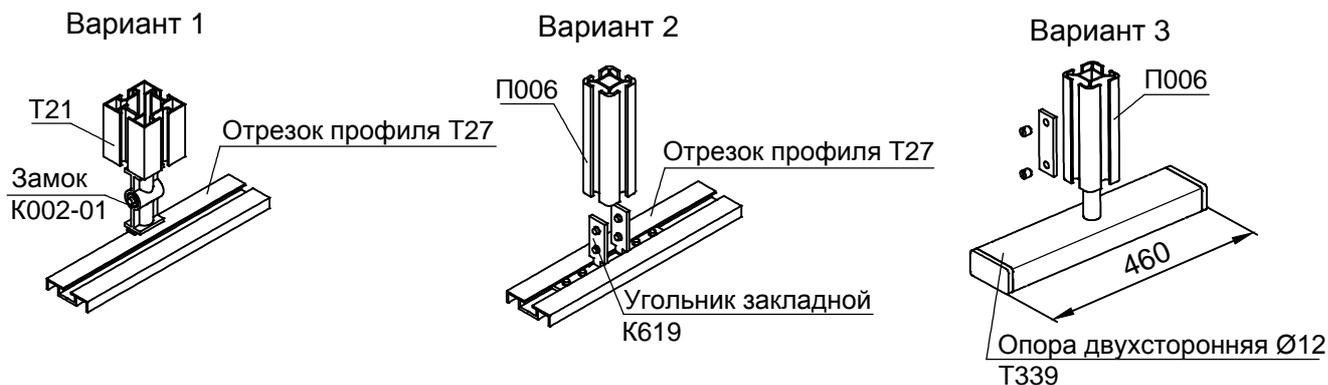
Перегородка на широких опорах с креплением к стене на расстоянии
